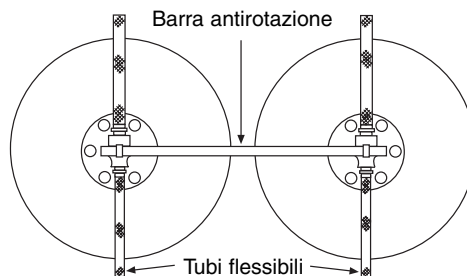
Installazione della barra antirotazione nell'aletta sulla testa.
